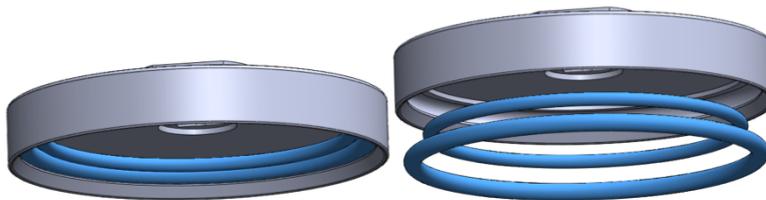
Desmontaje de las juntas tóricas del retenedor
